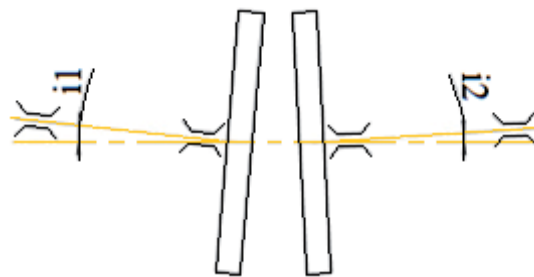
Расположение фрез под углом при наличии имеющихся зазоров в подшипниковых опорах под воздействием силы резания и нежёсткости корпусов фрез
